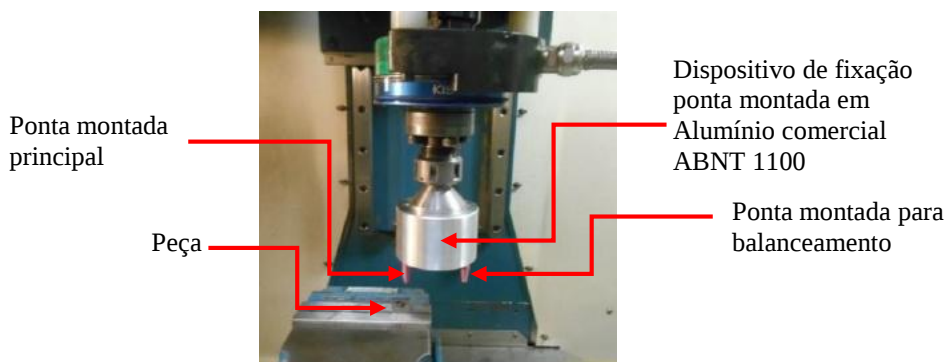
Vista geral do sistema de montagem suporte-ferramenta-peça.
